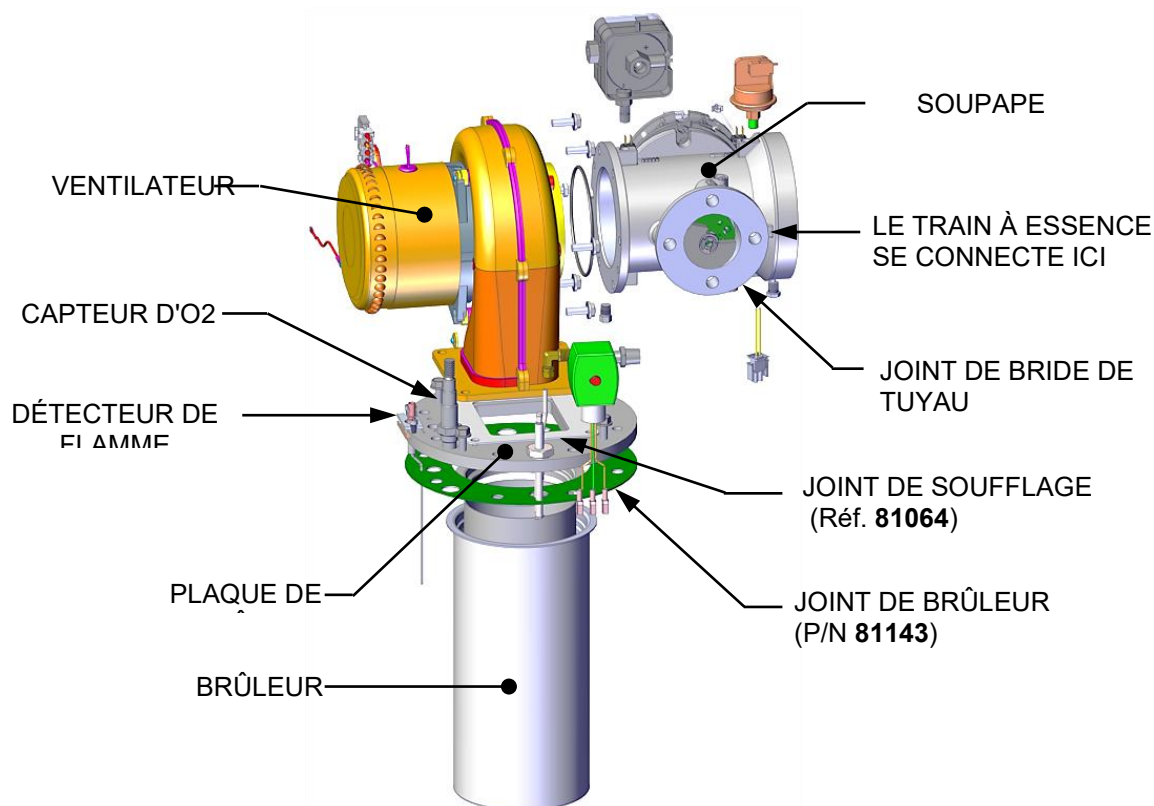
Vue éclatée de l'ensemble du brûleur – BMK750/1000
